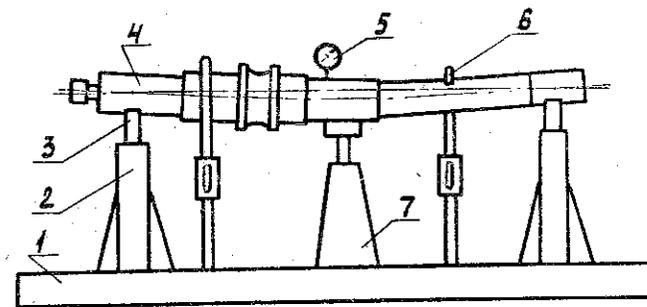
Приспособление для механической правки валов с местным нагревом: 1-основание; 2-стойка; 3-упор призматический с латунной подкладкой; 4-вал; 5-индикатор; 6-прижимная тяга; 7-горелка
